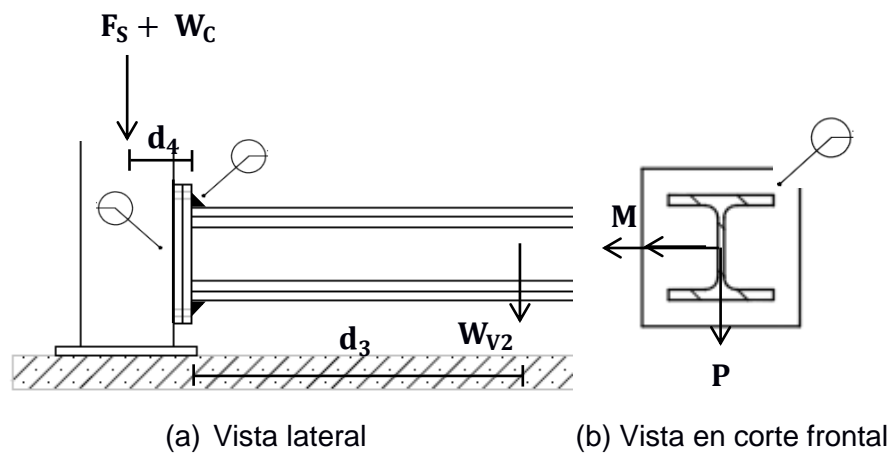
Fuerzas presentes en la unión de soldadura #4.
